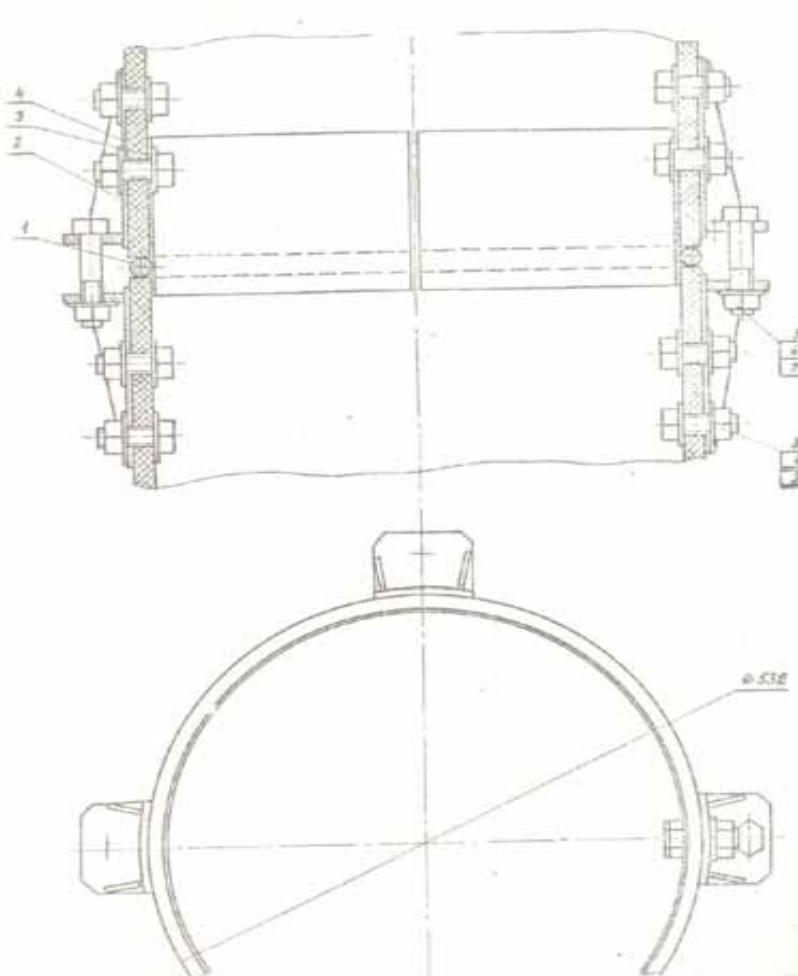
Стыковое соединение асбестоцементных труб (сборочный чертеж):
